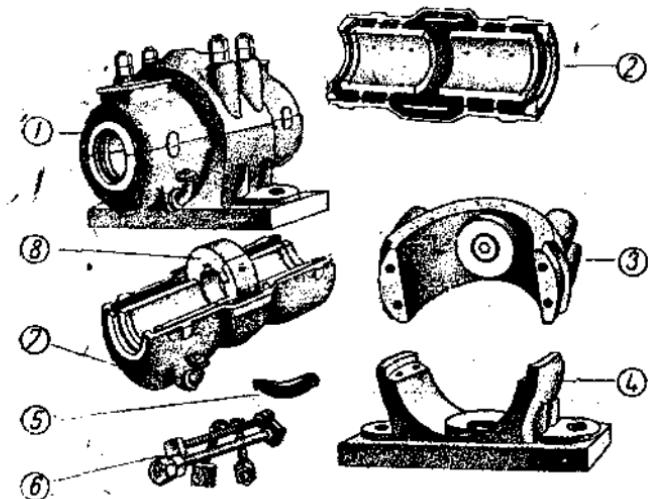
Подшипник Вюльфеля с шаровым движением, кольцевой смазкой и видимой циркуляцией масла.
